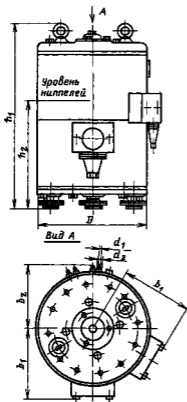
Габаритные и установочно-присоединительные размеры преобразователей ВПЧ
